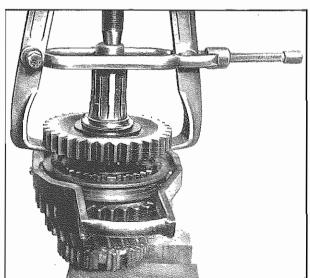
Ingranaggio della retromarcia Gear wheel reverse speed
